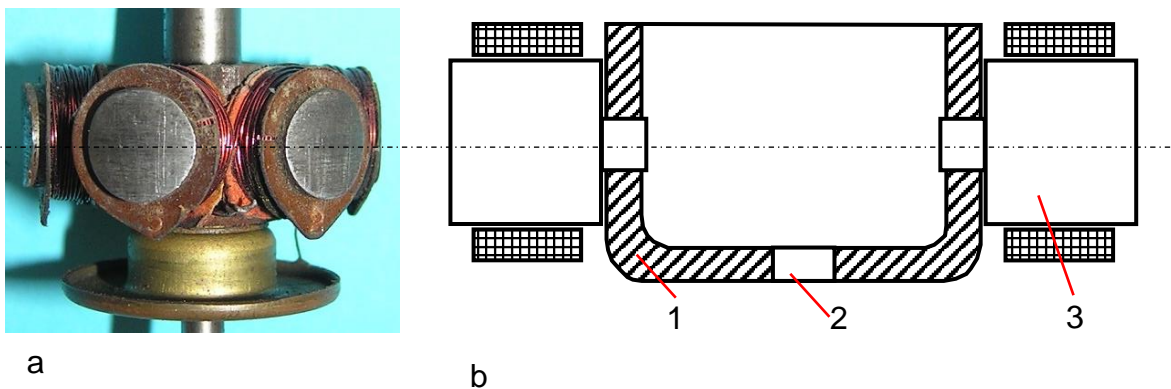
Ankerbau: a) Seitenansicht des Ankers mit der Schleifscheibe, b) Vereinfachter Querschnitt des Ankers: 1- Ankerjochtopf, 2- Wellenbohrung, 3- Spulenkerne
